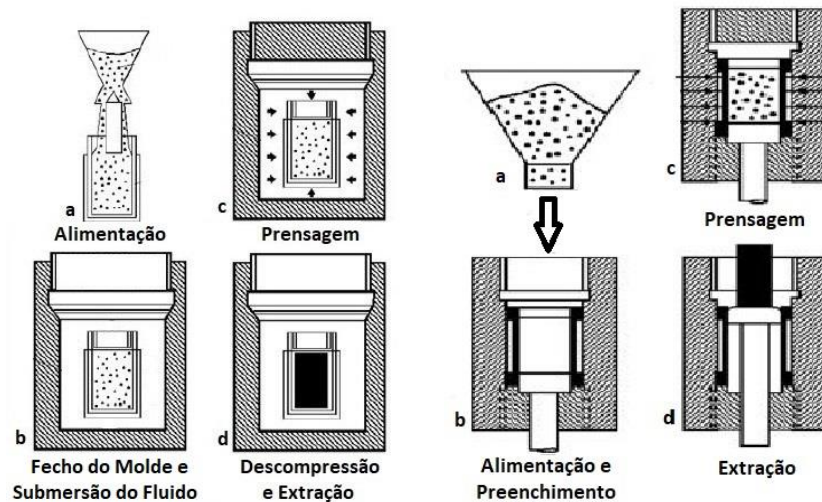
Prensagem isostática segundo a técnica do molde húmido (à esquerda) e seco (à direita) [32].
